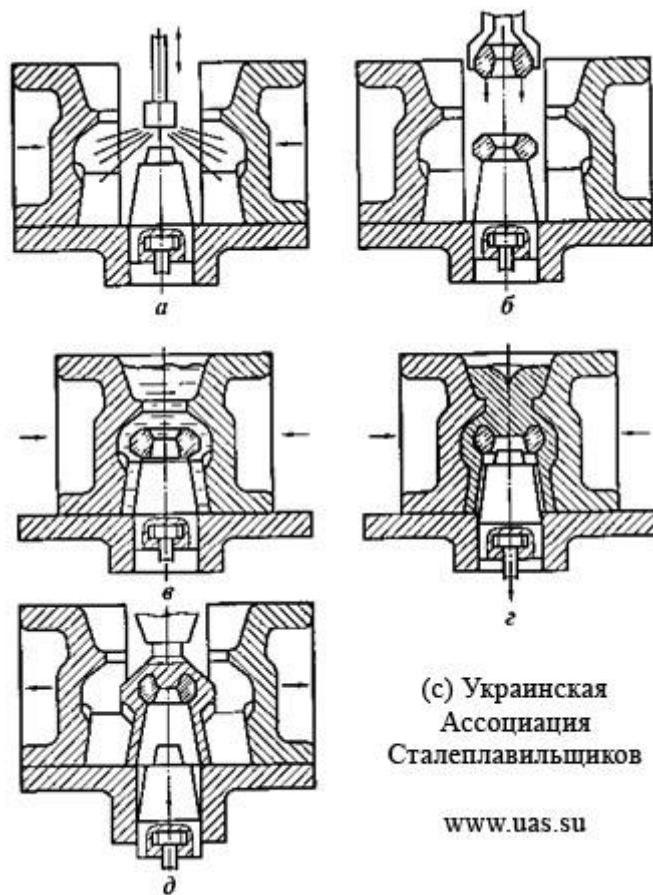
Последовательность изготовления отливки в кокиле (стрелки – направление движения деталей кокиля): а – покраска кокиля; б – установка стержней; в – сборка и заливка металла в форму; г – затвердевание отливки; д – разборка кокильной формы
